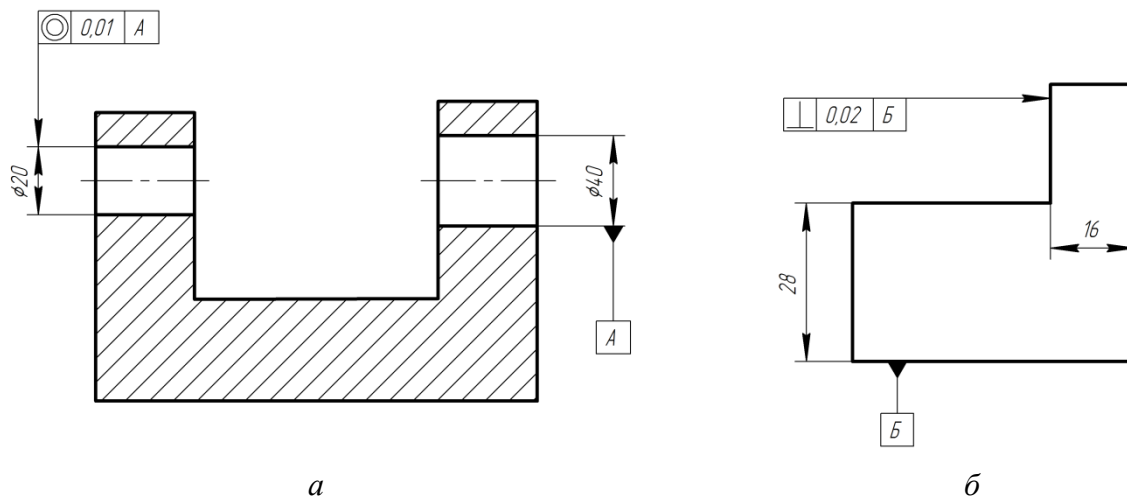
Примеры обозначения допусков расположения:
